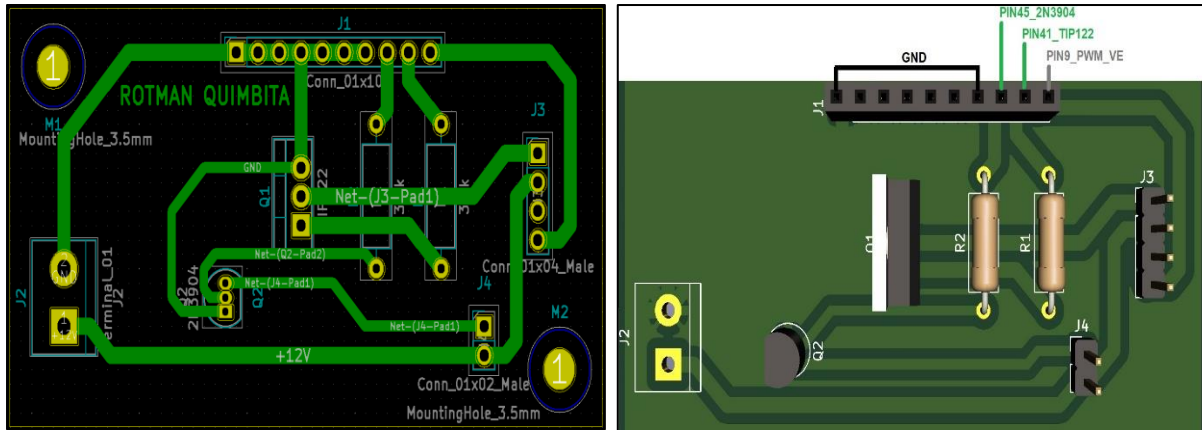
Módulo para ventiladores - diseño PCB y visualización 3D
